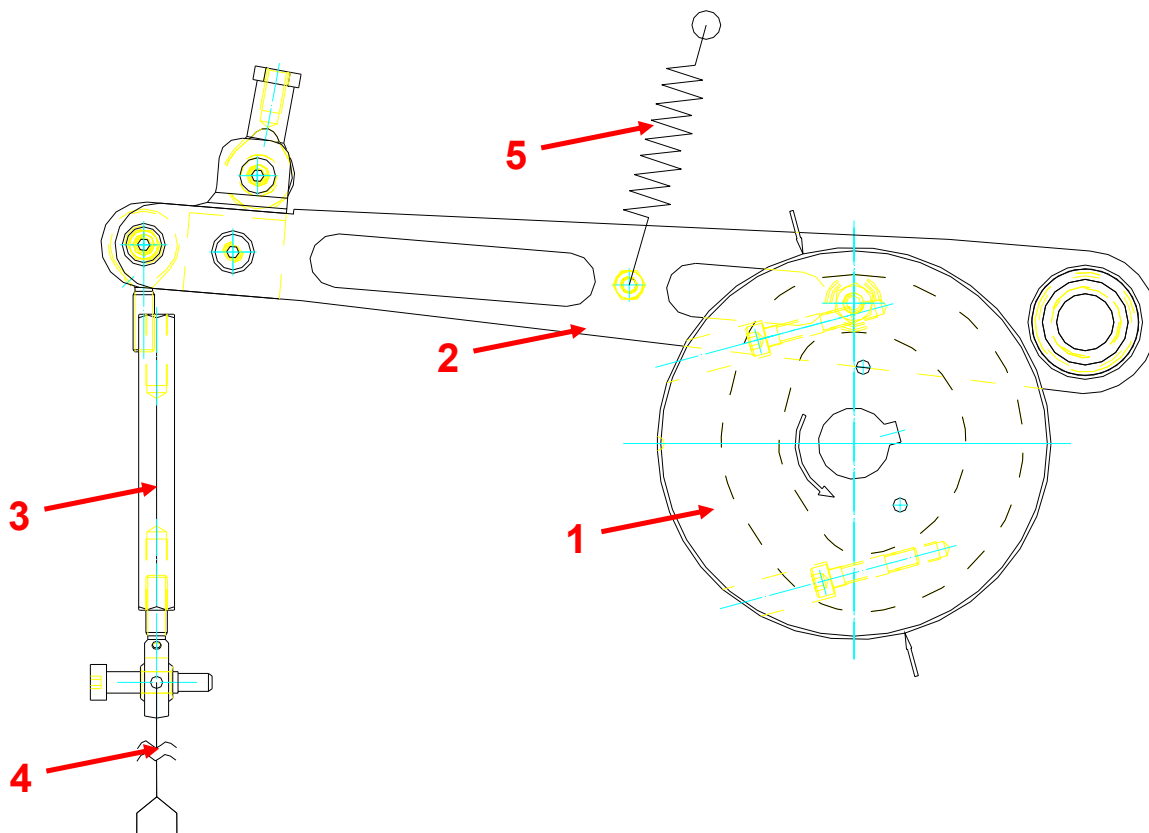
Montaj mecanism de inserare a pinilor în mufa conectoare
